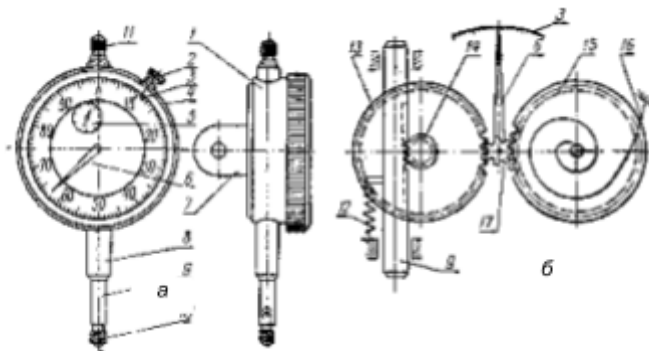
Індикатор нормального типу: 1 – корпус; 2 – стопорний гвинт; 3 – основна шкала; 4 – обичайка; 5 – шкала лічильника обертів великої стрілки; 6 – основна (велика) стрілка; 7 – вушко; 8 – втулка; 9 – вимірювальний стрижень; 10 – наконечник; 11 – головка; 12 – зворотня пружина; 13, 14, 15 і 17 – зубчасті колеса; 16 – спіральна пружина
